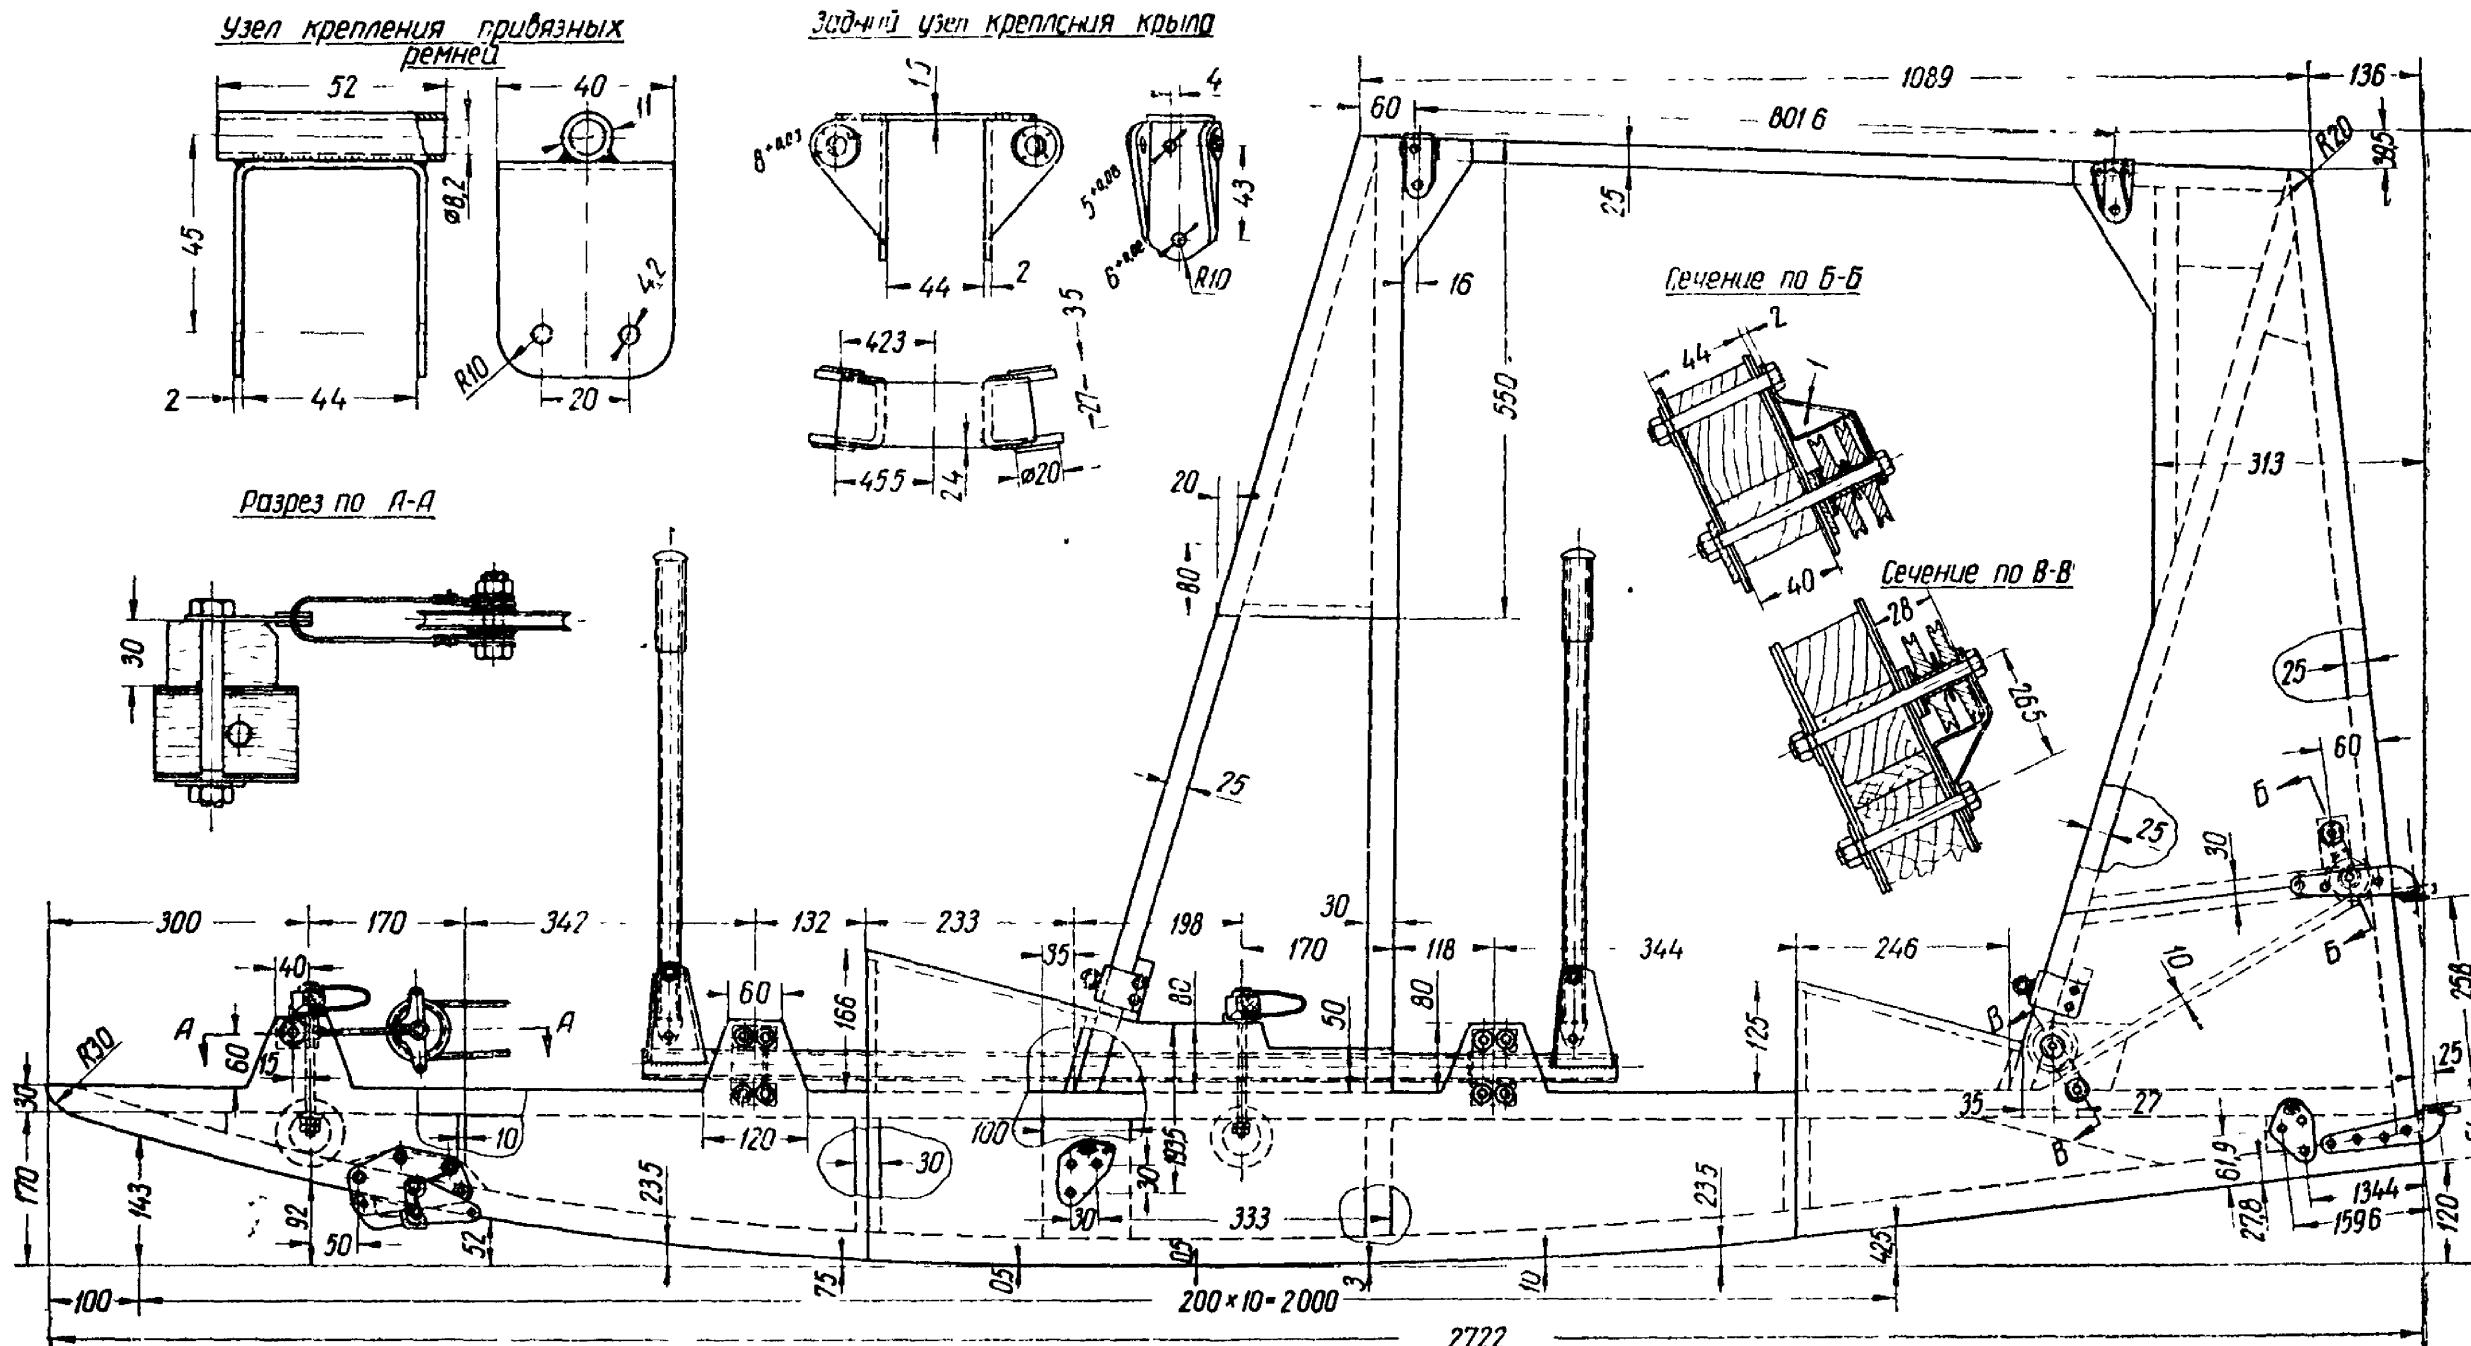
Планер А-2 Ферма и установка металлических узлов на ферме
